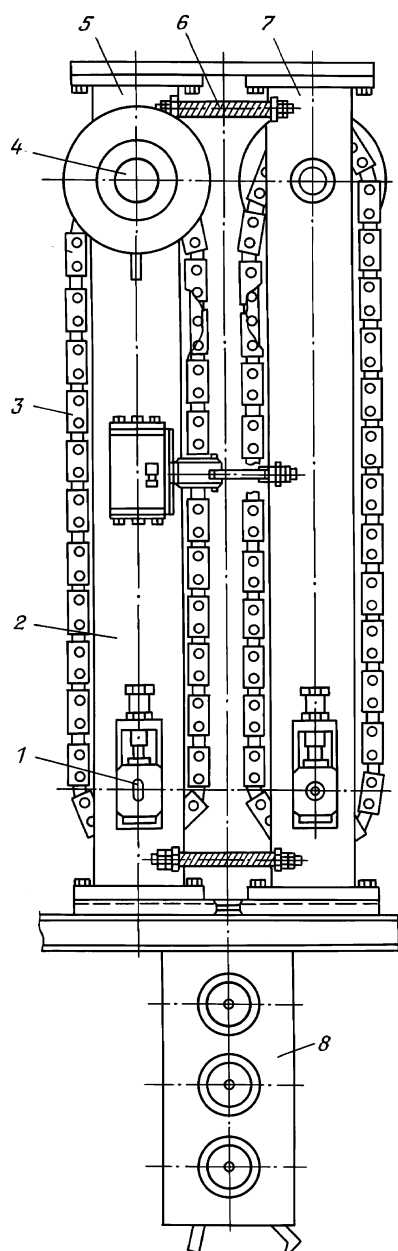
Схема транспортера с двумя цепями и механическим регулированием прижима плашек и натяжения цепей:
